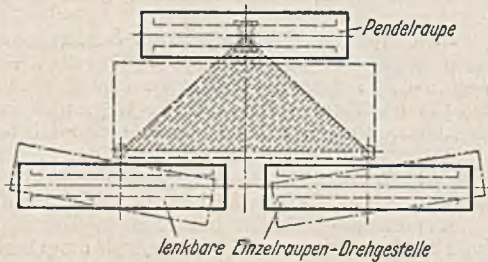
Grundriß eines lenkbaren Drei-Raupen-Fahrgestelles für umzubauende Schienenbagger.
